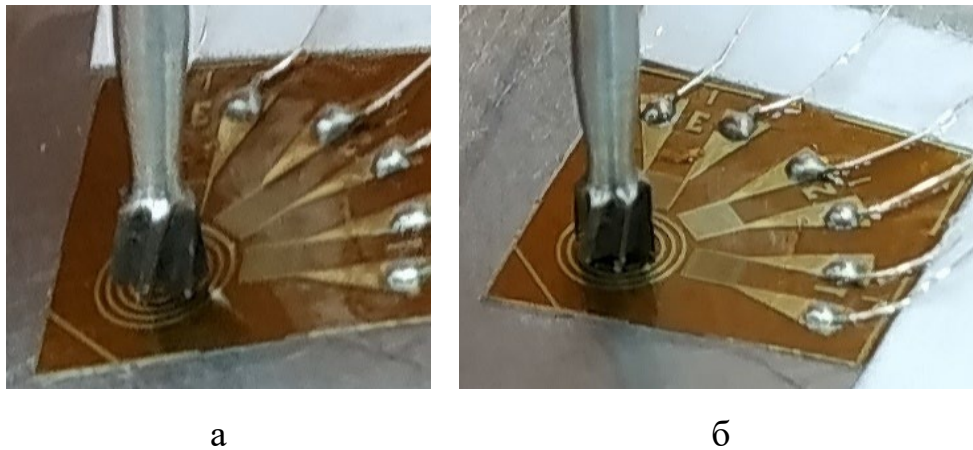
Розташування свердла відносно вимірюваної поверхні: а – з перекоосом;
